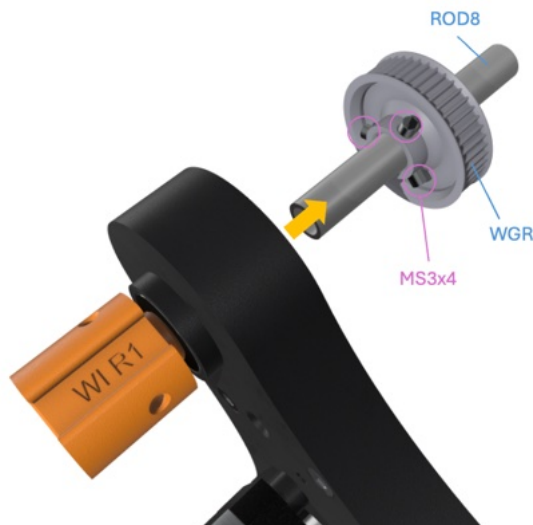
Rewinder-Chassis Montageschritt 8.
